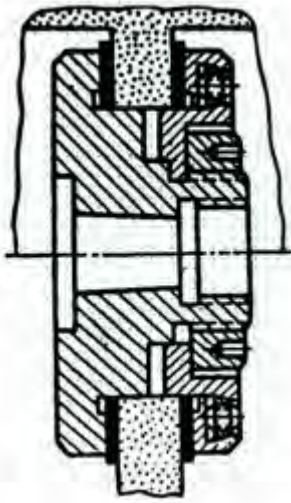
Кріплення шліфувального круга в перехідних фланцях
